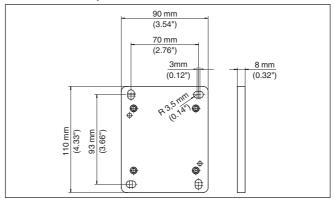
Plantilla de taladros - montaje mural (carcasa externa)
